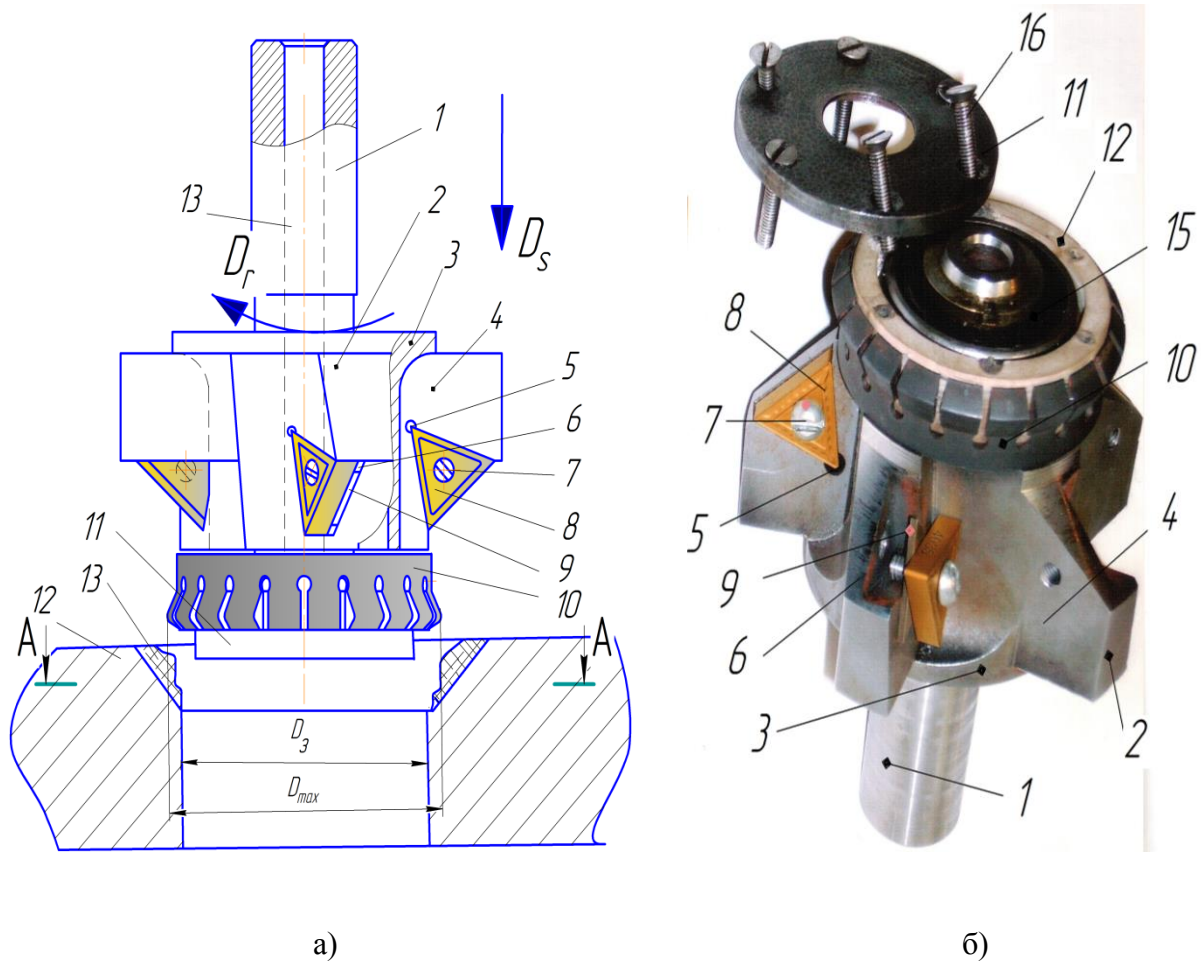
Схема зенкерования конического отверстия виброустойчивым инструментом (а) и фото инструмента (б): 1 – посадочная ступень корпуса, 2 – ступень корпуса, 3 – предохраняющая шейка, 4 - стружечная канавка, 5 – малое отверстие, 6 – гнездо под режущую пластину, 7 – винт, 8 – режущая пластина, 9 – опорная пластина, 10 – демпфирующий элемент, 11 – крышка, 12 – заготовка, 13 – наплавленный слой износостойкого материала, 14 - резиновое кольцо, 15 – шарикоподшипник, 16 – винт.
